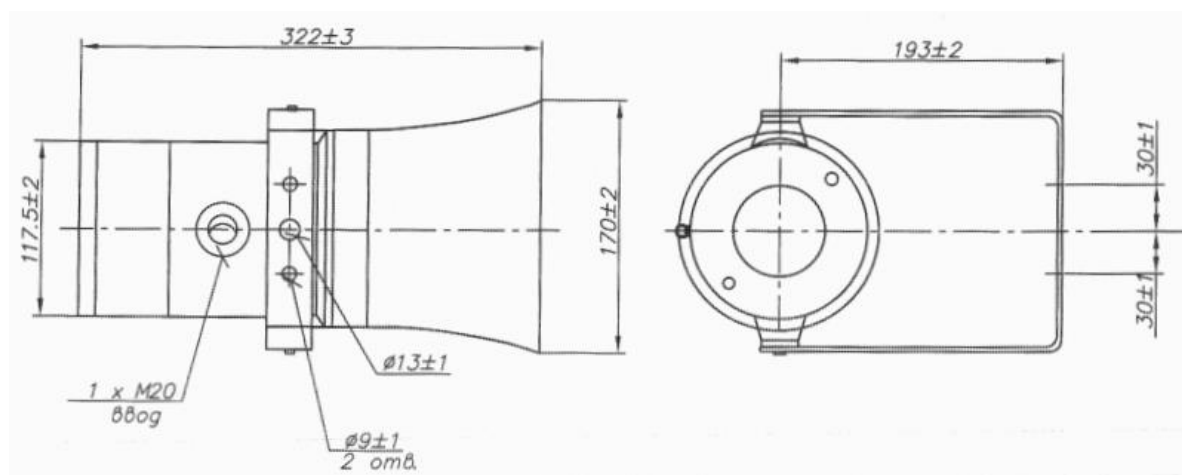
Ескіз установки звукового оповісвача ДВЗДЗВП04
